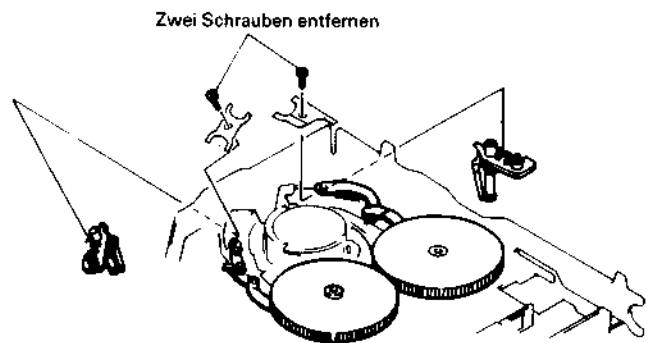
Ausbau der Führungsrollen-Grundplatte
